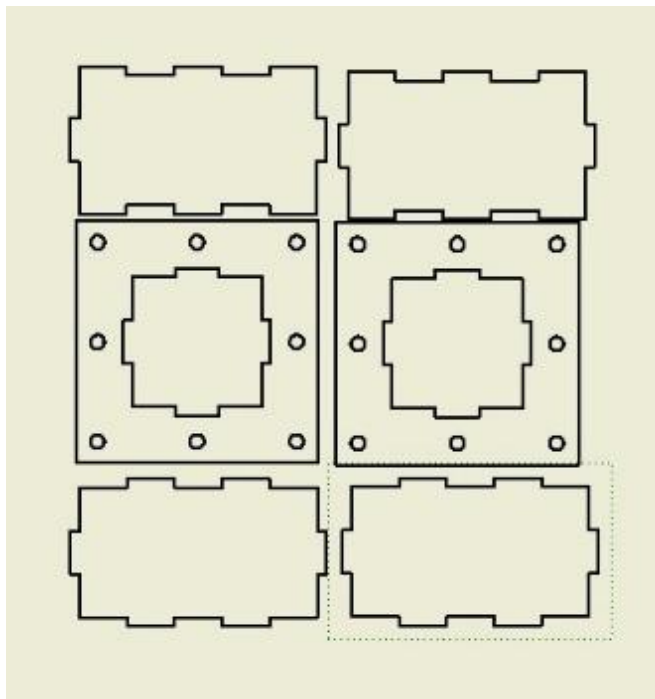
Tvar desky, která se používá pro kolmý spoj.
